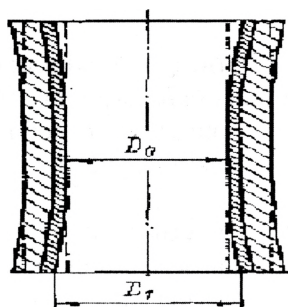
Деформация полого цилиндра при поверхностной закалке внутренней поверхности
